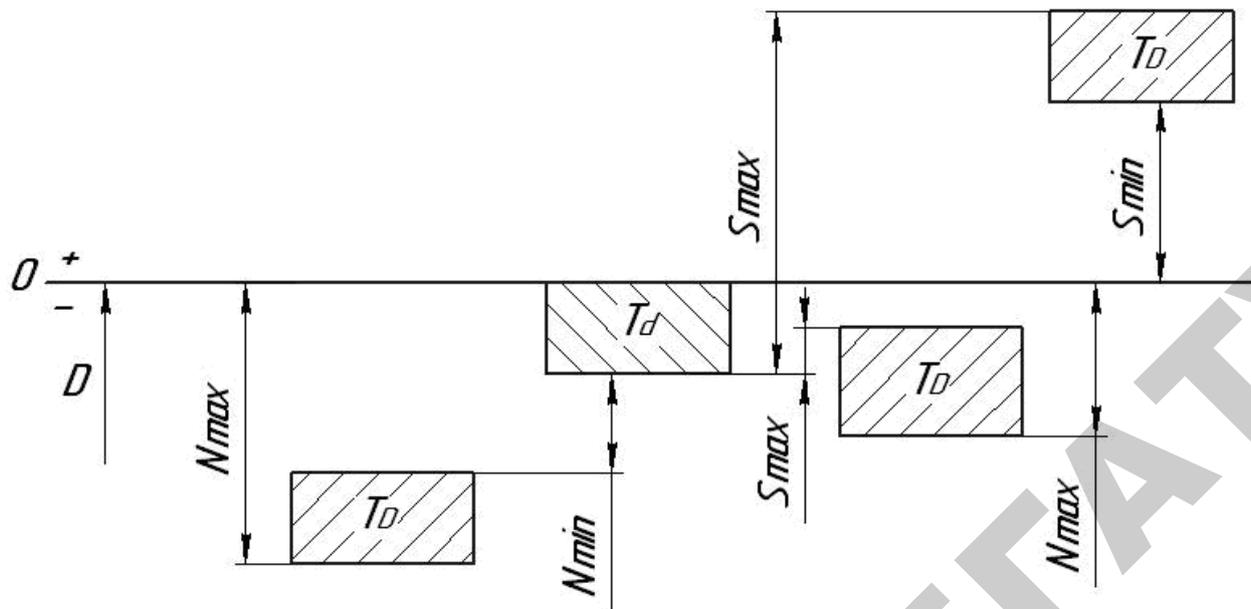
Посадки в системе вала и схемы расположения полей допусков
